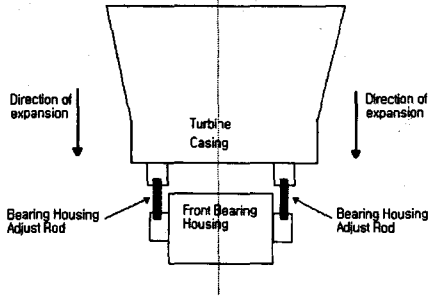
터빈케이싱 및 베어링 하우스 팽창방향
